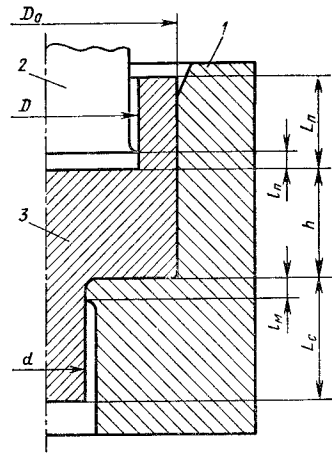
Схема комбинированного выдавливания: 1 — матрица; 2 — пуансон; 3 — заготовка
